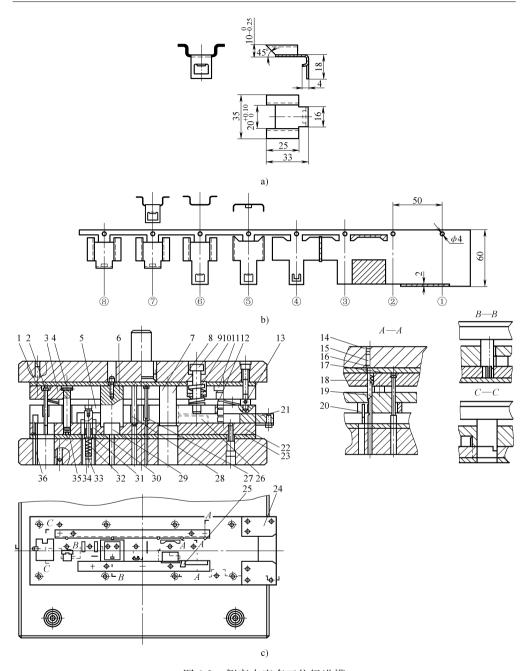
侧弯支座多工位级进模 a) 工件图 b) 排样图 c) 模具结构图
